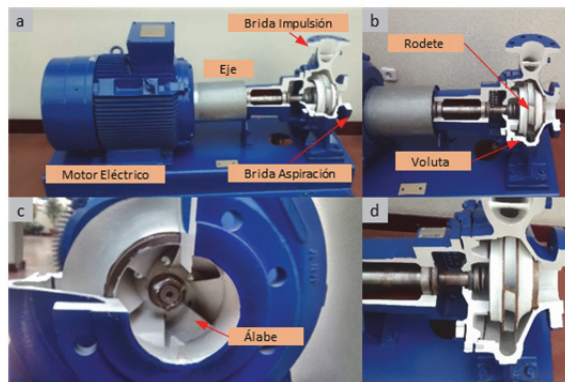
(a) Vista general bomba seccionada. (b) Detalle bloque hidráulico: voluta, eje y rodete. (c) Vista frontal rodete. (d) Vista longitudinal rodete
